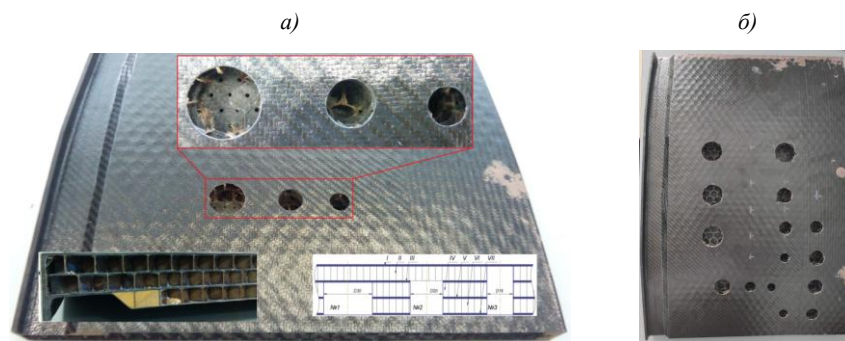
Образец семислойной сотовой конструкции из ПКМ с искусственными дефектами
